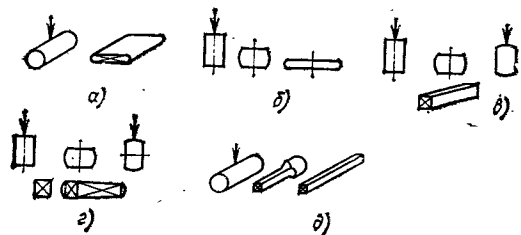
Схемы ковки (изготовления) заготовок из сплавов цветных металлов:
